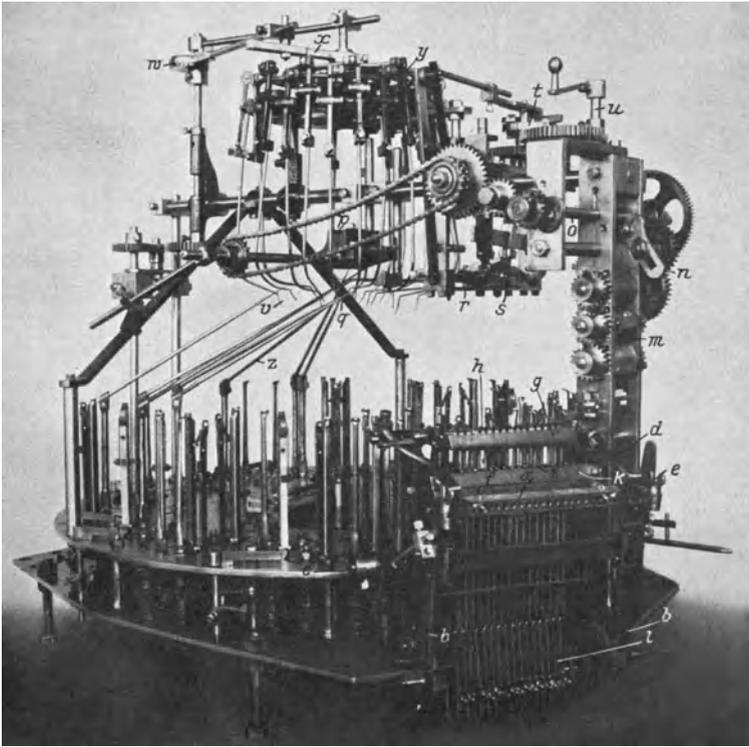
Zweifädige Spitzenklöppelmaschine.
